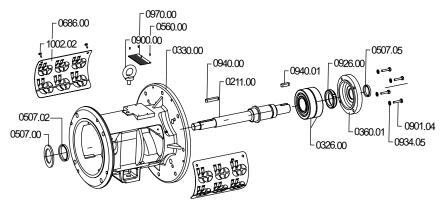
Опора подшипника для двигателей типоразмера до 160 включительно
